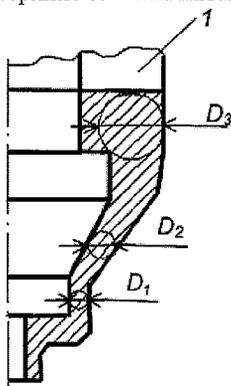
Конструкция литой детали, обеспечивающая направленное затвердевание
